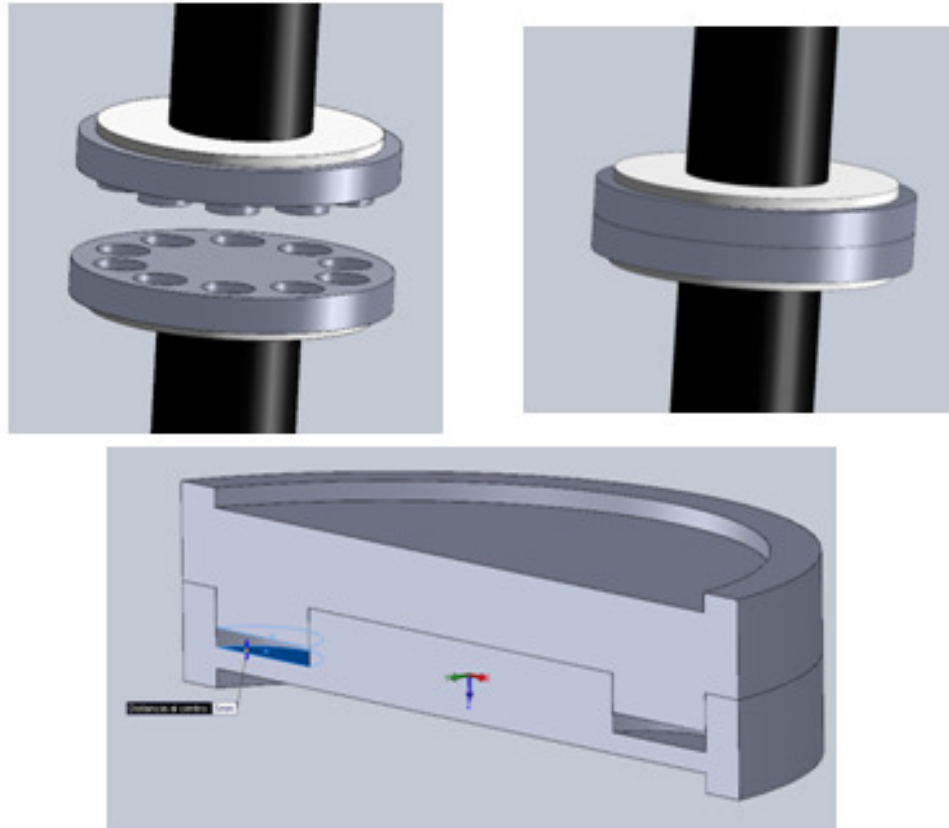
Ensamble de moldes para compresión a discos de compresión de prensa (Modelación CAD Solidworks)
